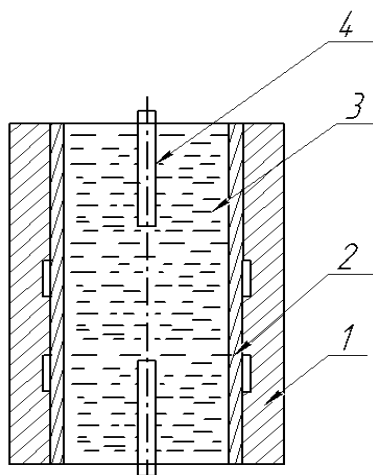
Электрический разряд между двумя электродами в объеме рабочей передаточной среды над заготовкой, установленной в формообразующей полости инструмента: 1 - матрица, 2 - заготовка кольцевая, 3 - передающая среда (вода), 4 – электрод
